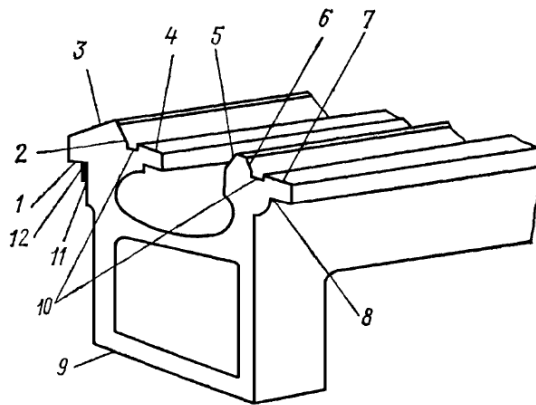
Напрямні станини токарно-гвинторізного верстата мод. 1К62
